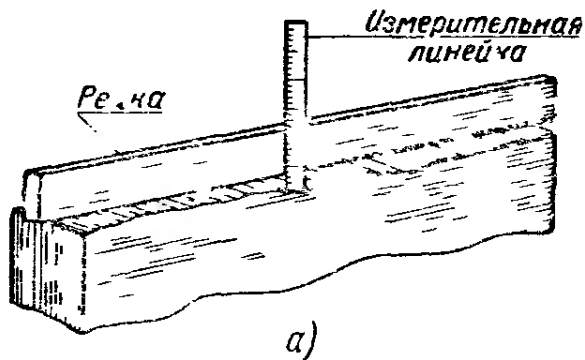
Проверка качества подготовки кромок под сварку
